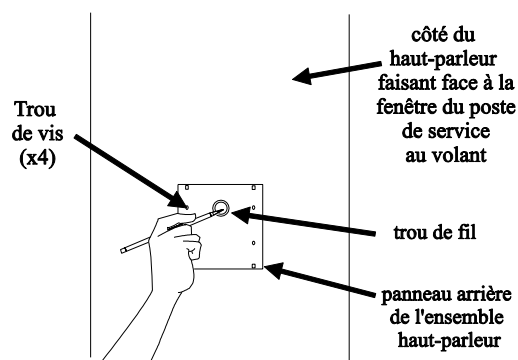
Faites une marque sur le poteau de haut-parleur ou le panneau de menu à travers le trou de fil du panneau arrière du haut-parleur SP2500LP
